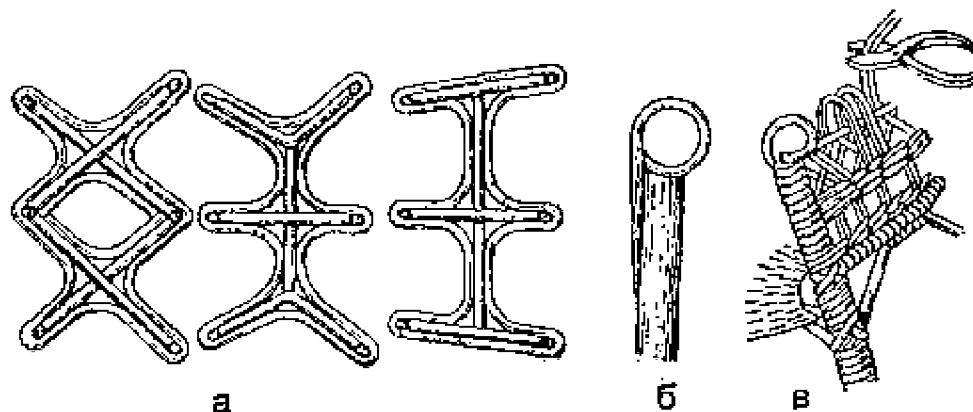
Изготовление дивана: а - крестовина; б - дужка; в - плетение валика
